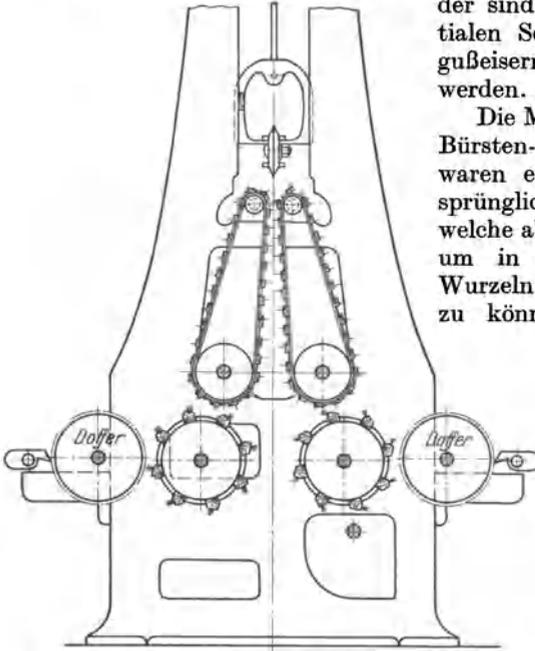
Schema einer Bürsten-Doffer-Hechelmaschine.
